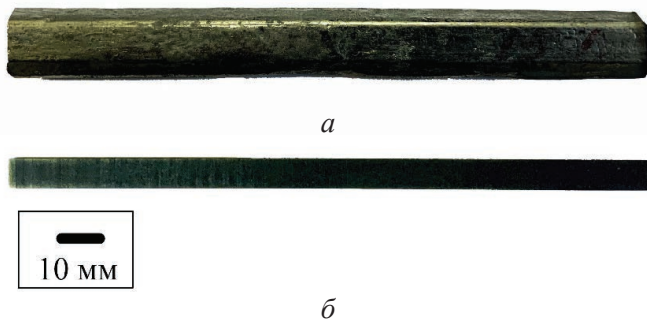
Форма и размеры образцов из сплава TiNiHf:
